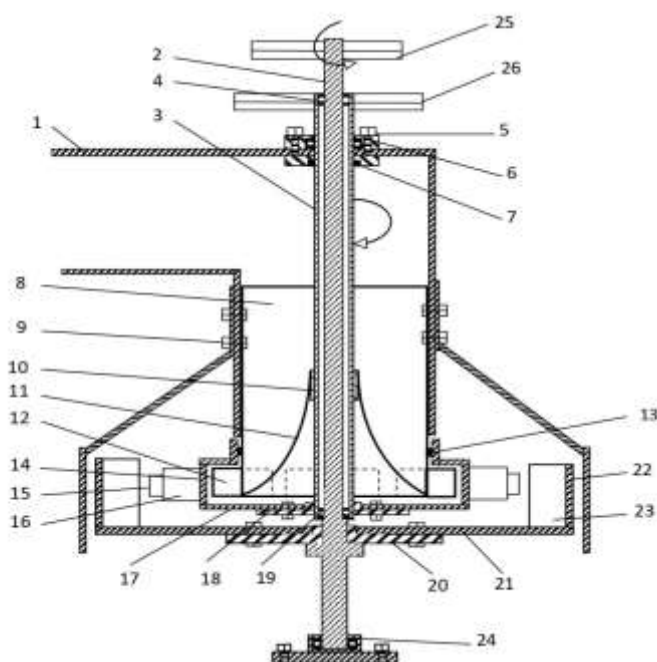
Общий схематический вид контрроторного гидроагрегата: 1 - входной поток; 2 - внутренний вал; 3 - внешний вал; 4 - подшипник между валами; 5 - крепежные болты корпуса подшипника; 6 - подшипник; 7 - сальник; 8 - направляющая лопатка; 9 - болты; 10 - верхний гидравлический подшипник; 11 - внутренний соосный конус; 12 - направляющие рабочие колёса; 13 - резиновый сальник; 14 - рабочее колесо цилиндра; 15 - конфузурная насадка для выпуска воды; 16 - отводные каналы; 17 - основание диска; 18 - опора с насадками; 19 - конусная опора; 20 - диск с цапфой для крепления активного рабочего колеса; 21 - диск активного рабочего колеса; 22 - внутреннее и наружное кольца; 23 - лопасти; 24 - подшипник корпуса; 25 - шкив активного рабочего колеса; 26 - шкив реактивного рабочего колеса.
